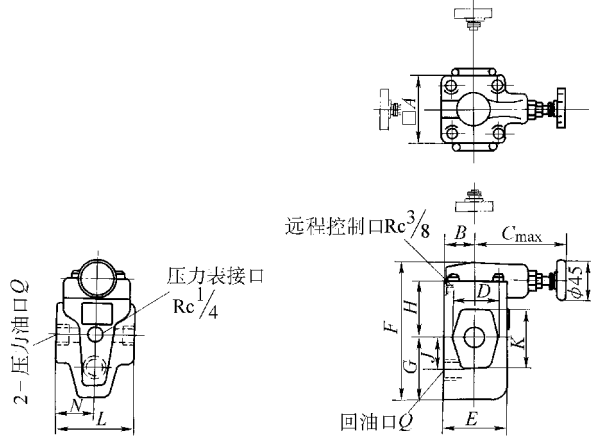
BT 型先导式溢流阀外形尺寸图
